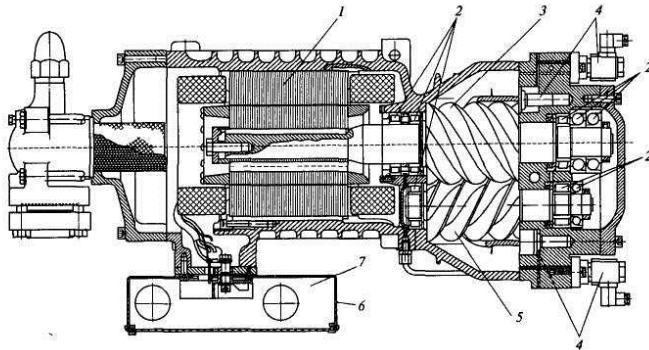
Гвинтовий безсаліниковий компресор: 1 – вбудований електродвигун; 2 – підшипники; 3 – ведучий ротор; 4 – пристрій регулювання продуктивності (розвантажений старт); 5 – ведений ротор; 6 – клемна коробка; 7 – пристрій захисту електродвигуна.
